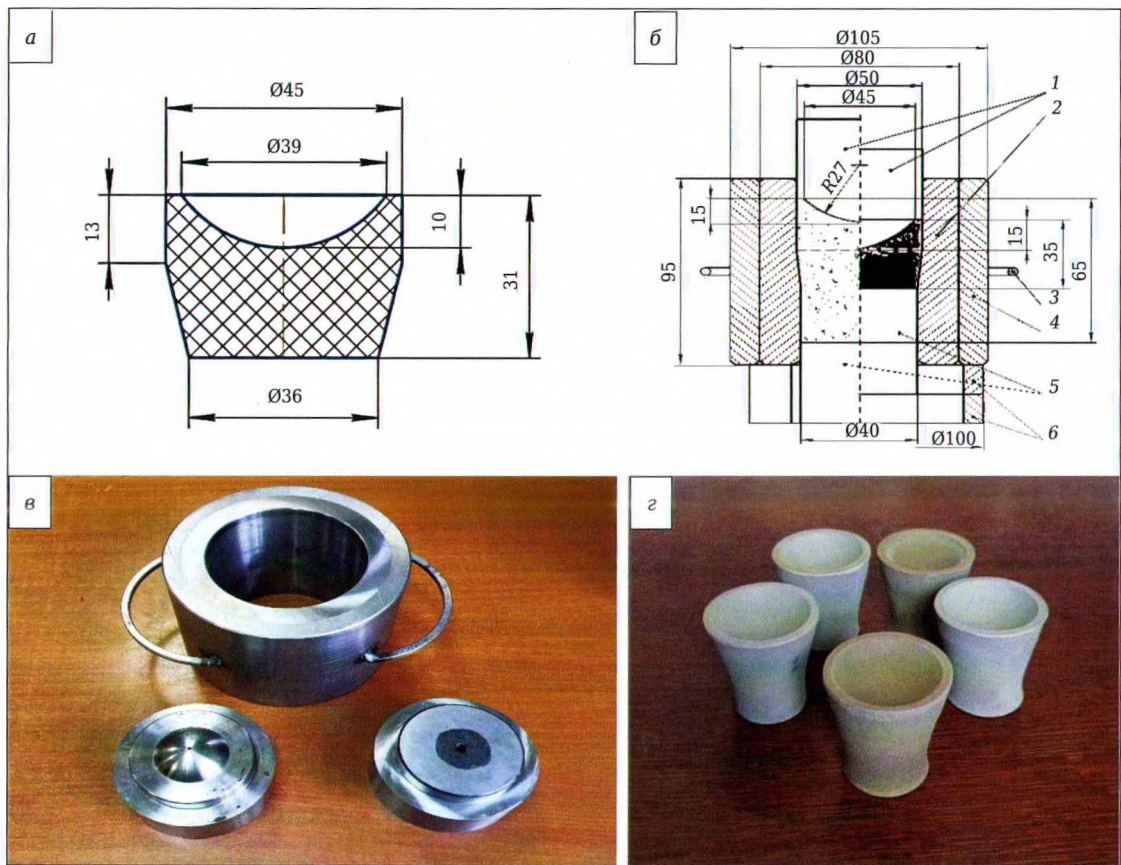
Конструкция изделий — купели (а), пресс-формы (б) и технологическая оснастка — пресс-форма (в) для формования заготовок купелей (з): 1 — пуансон верхний; 2 — матрица; 3 — ручка; 4 — бандаж; 5 — пуансон нижний; 6 — кольцо упорное
